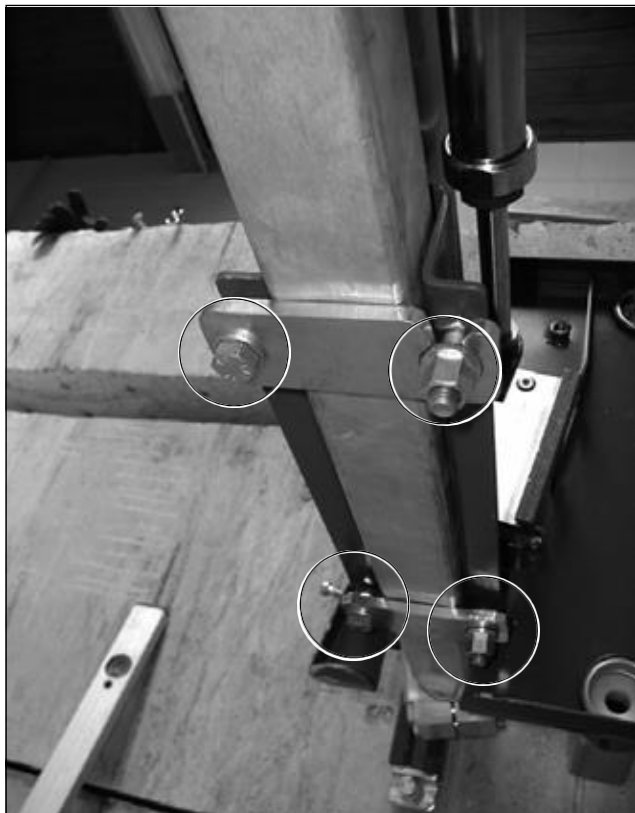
Schwenkgelenk, Montagerohr auf dem CSA•100 Präzisions-Schwenkfuß ausrichten
